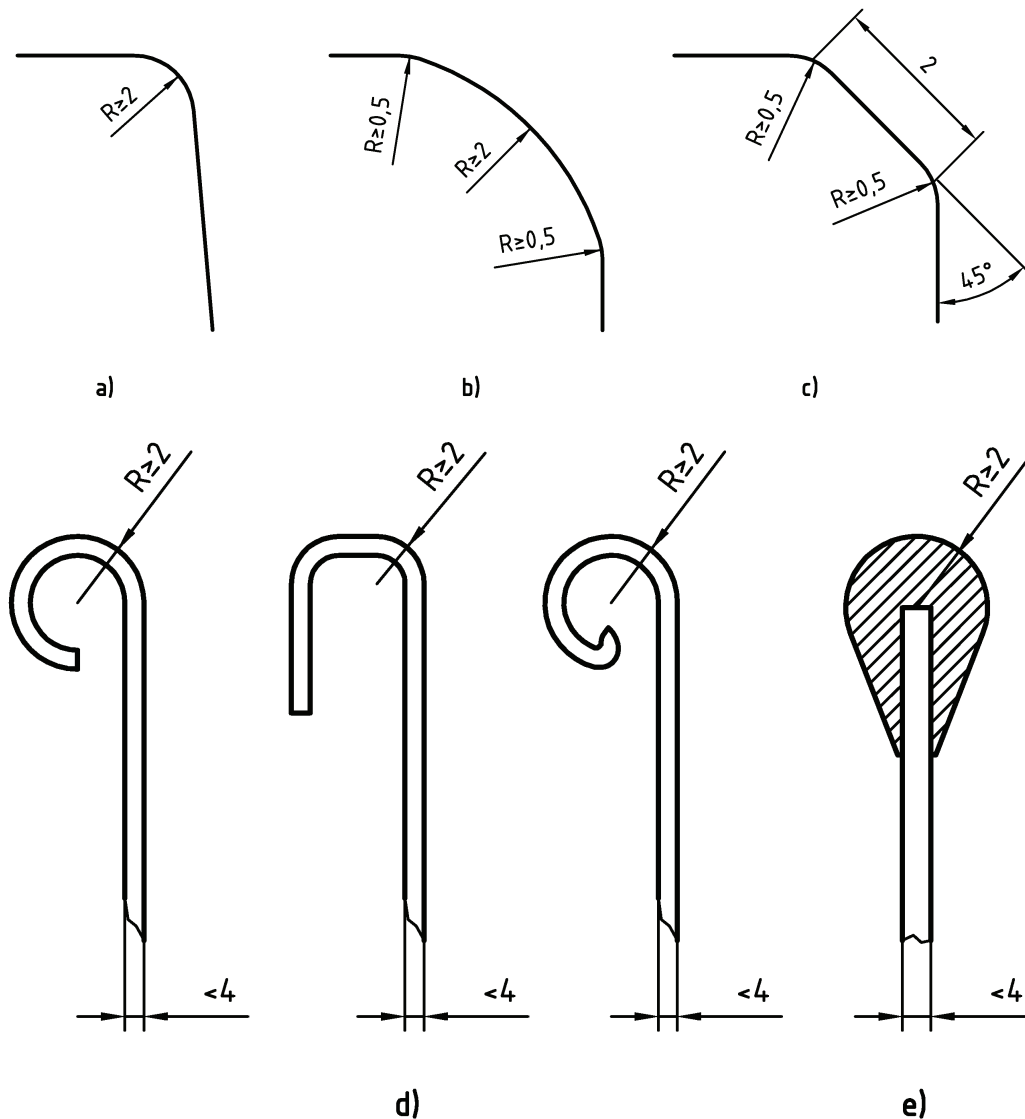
Beispiele für Mindeststradien von Kanten und Ecken
